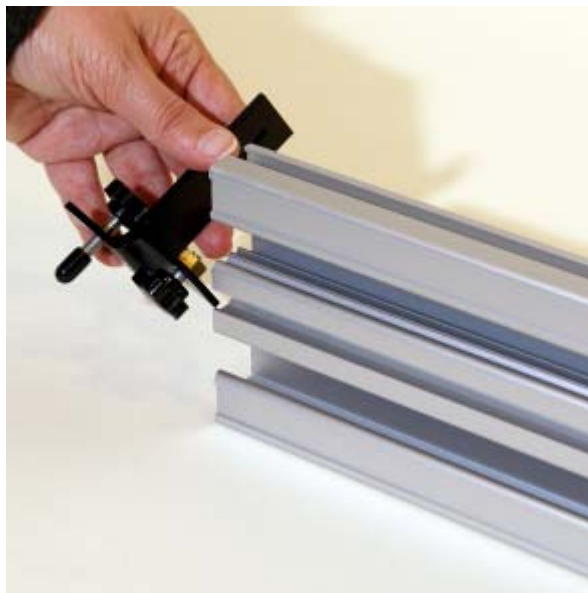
Colocação do apoio pontual na ranhura central na parte inferior do trilho de rolagem
